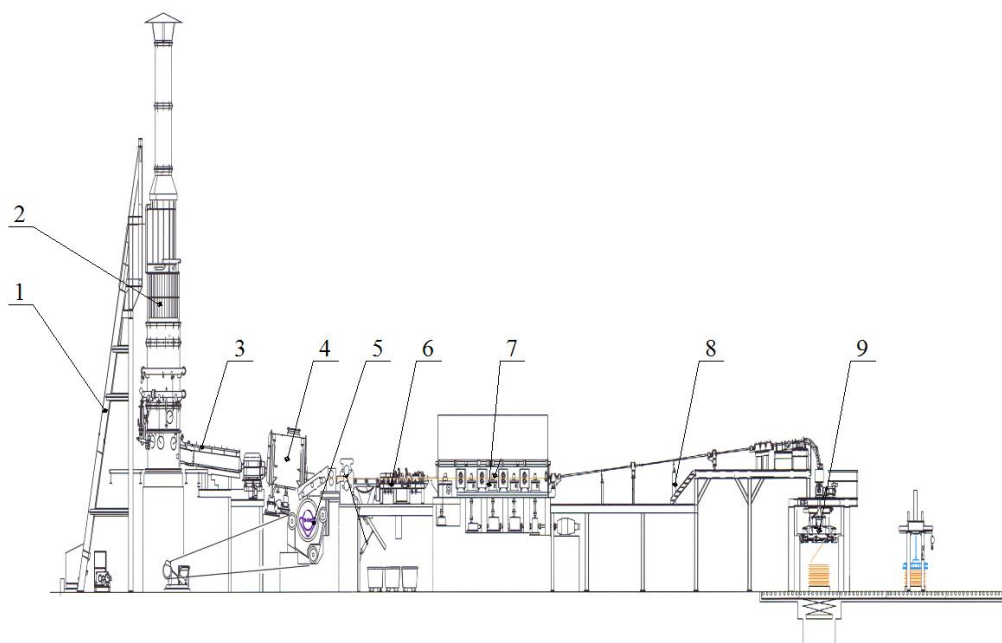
Принципиальная схема установки SOUTHWIRE: 1 – скиповый подъемник; 2 – плавильная печь; 3 – разливочный желоб; 4 – раздаточная печь; 5 – машина непрерывного литья; 6 – машина подготовки; 7 – прокатный стан; 8 – машина окончательной обработки; 9 – моталка
